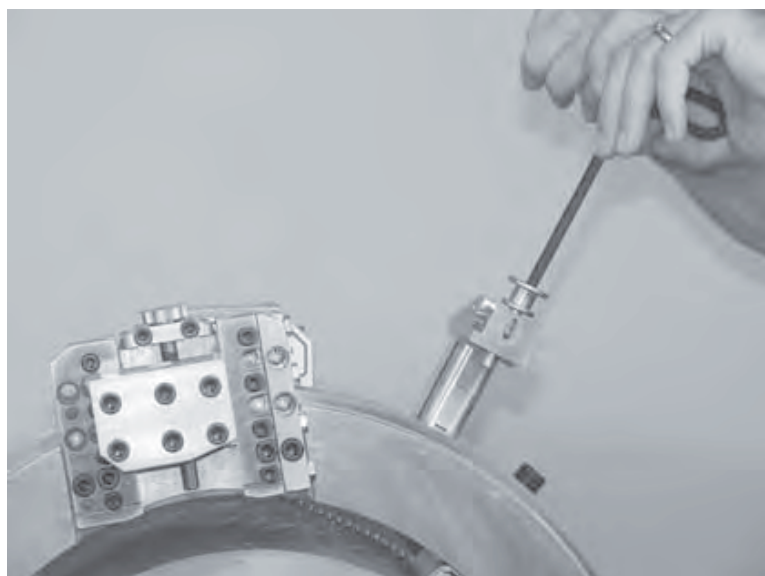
Механизм включения/выключения подачи резца показан с 2 шт. удлинительными блоками согласно «верхнему» положению суппорта.
